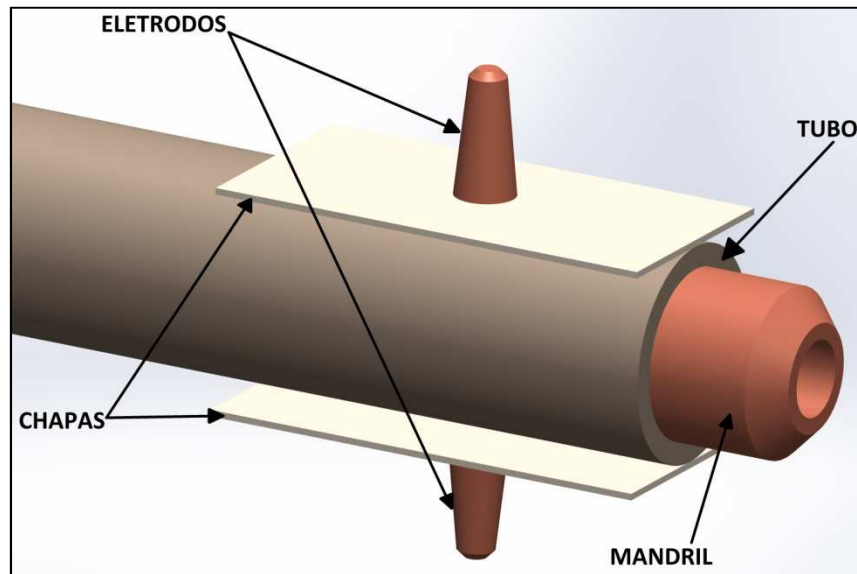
Corpo de prova de solda a ponto e os eletrodos [Fonte: o Autor].
